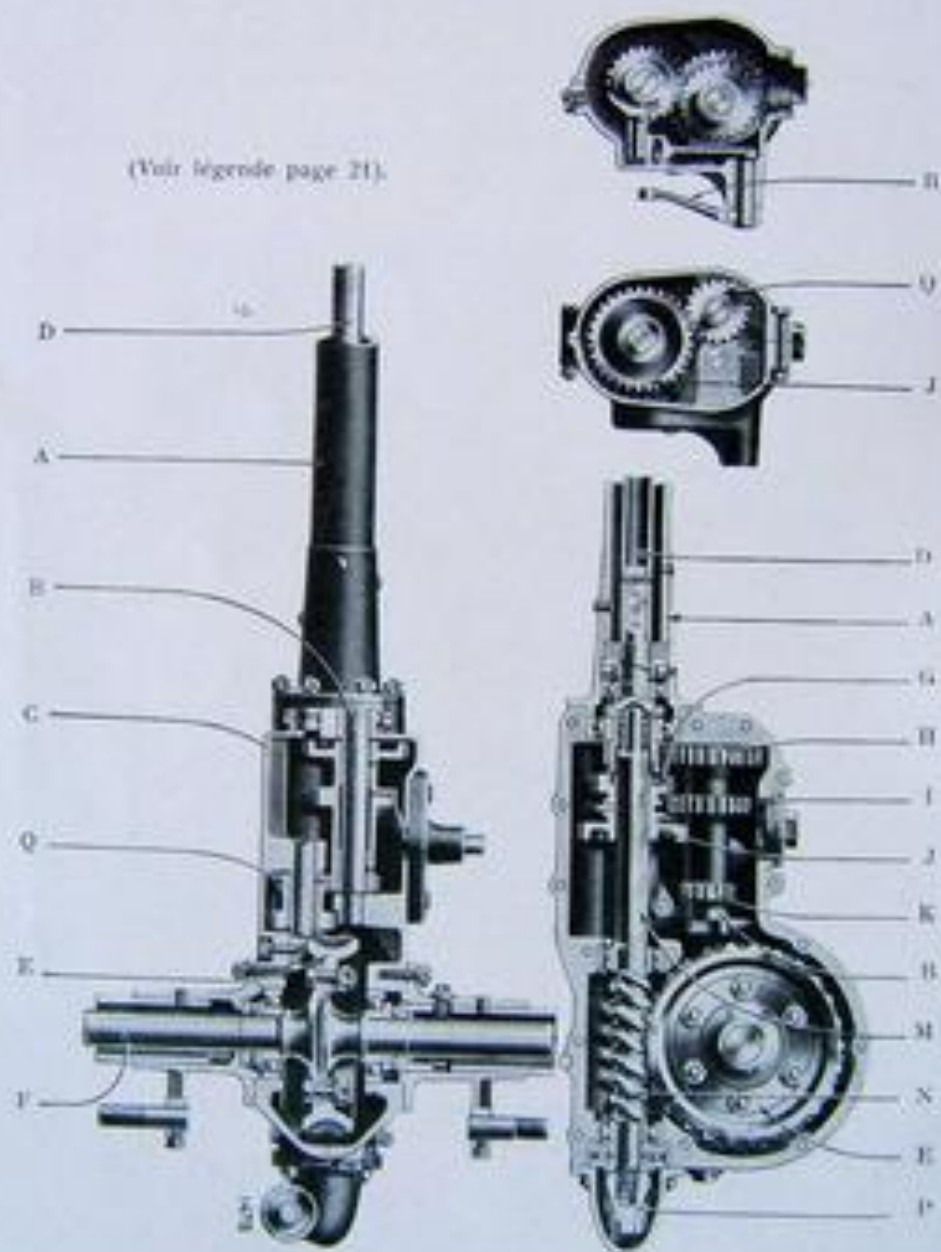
COUPES DU CHANGEMENT DE VITESSE ET DU PONT ARRIÈRE.
